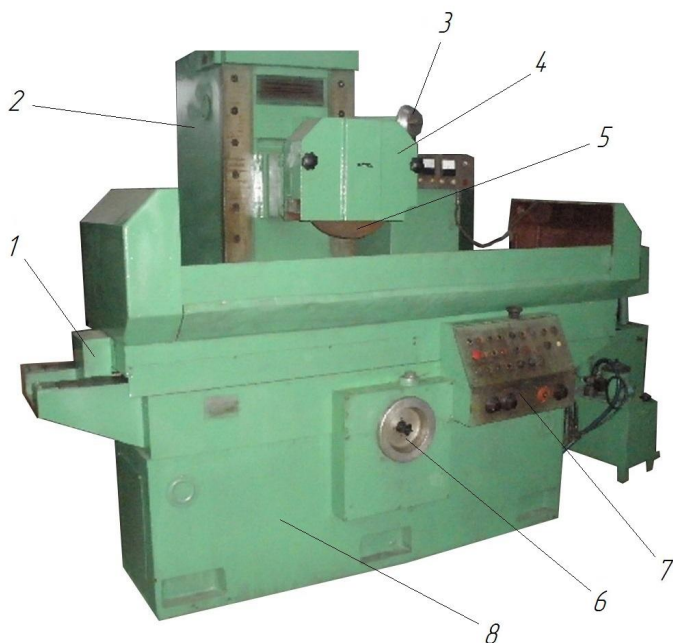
Плоскошлифовальный станок с прямоугольным столом
